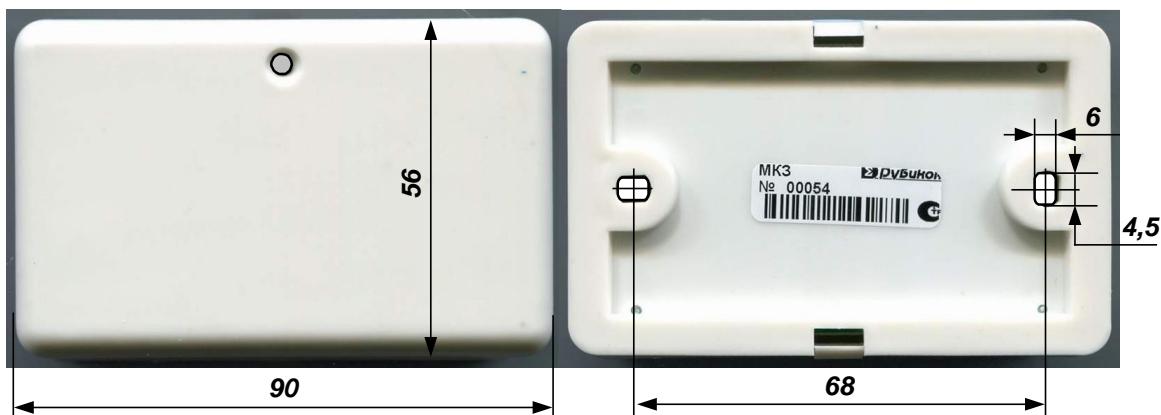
Габаритные и присоединительные размеры корпуса МК3
